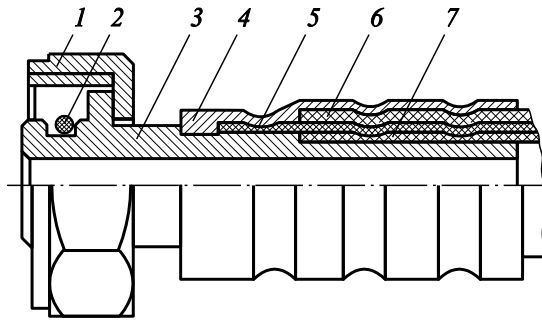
Заделка резинового рукава с металлической оплеткой ниппельного соединения:
